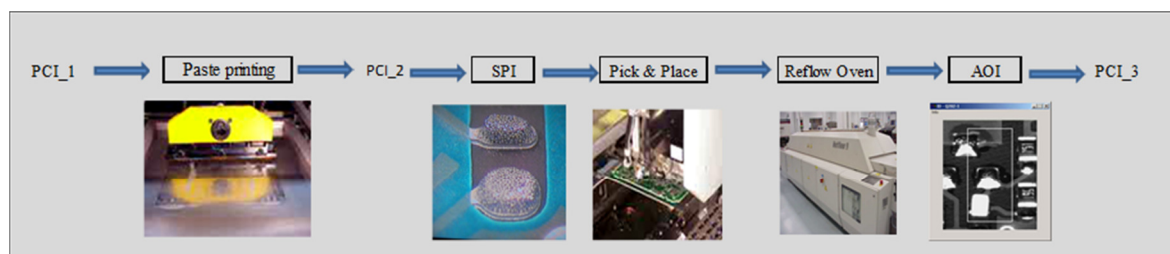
Diagrama do processo de inserção automática e soldadura *reflow
